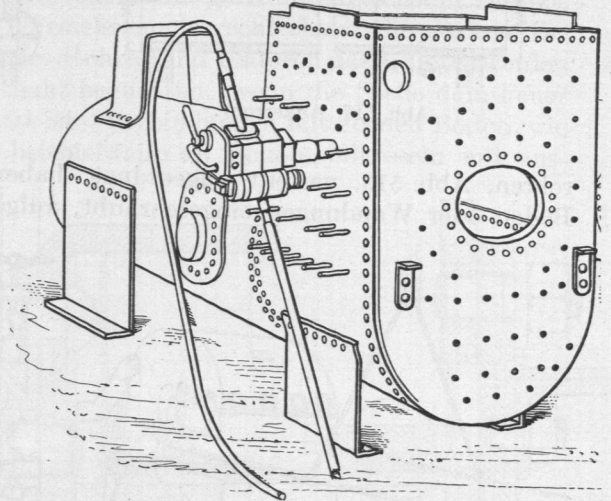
Einschneiden des Stehbolzengewindes und Einschrauben der Stehbolzen.
